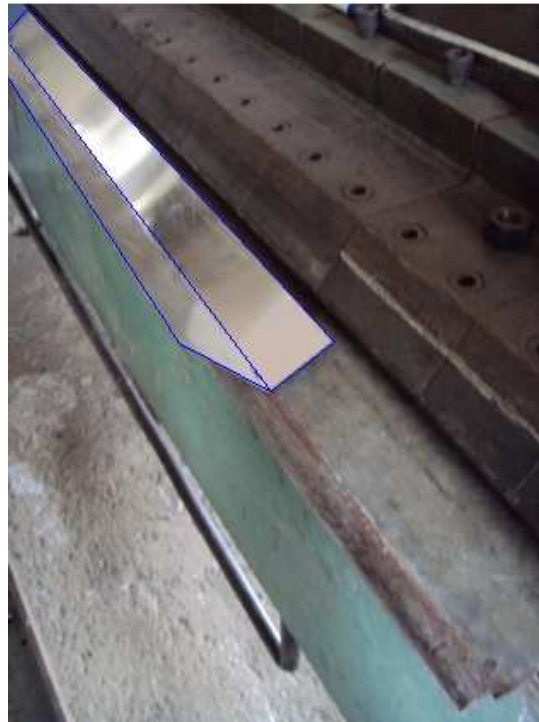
Inserción de la herramienta junto con la lámina de aluminio en la máquina dobladora
